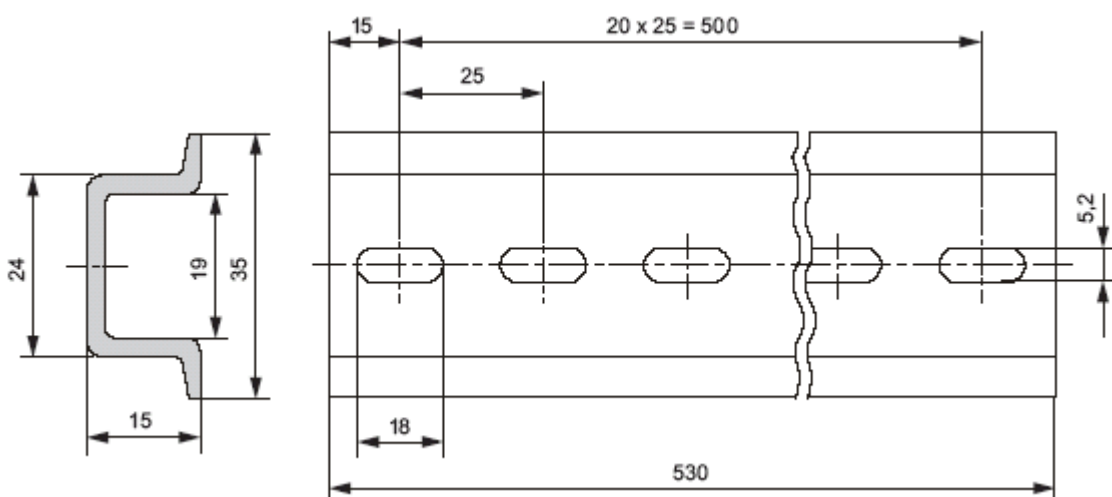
Габаритный чертеж 530-миллиметровой стандартной профильной шины
